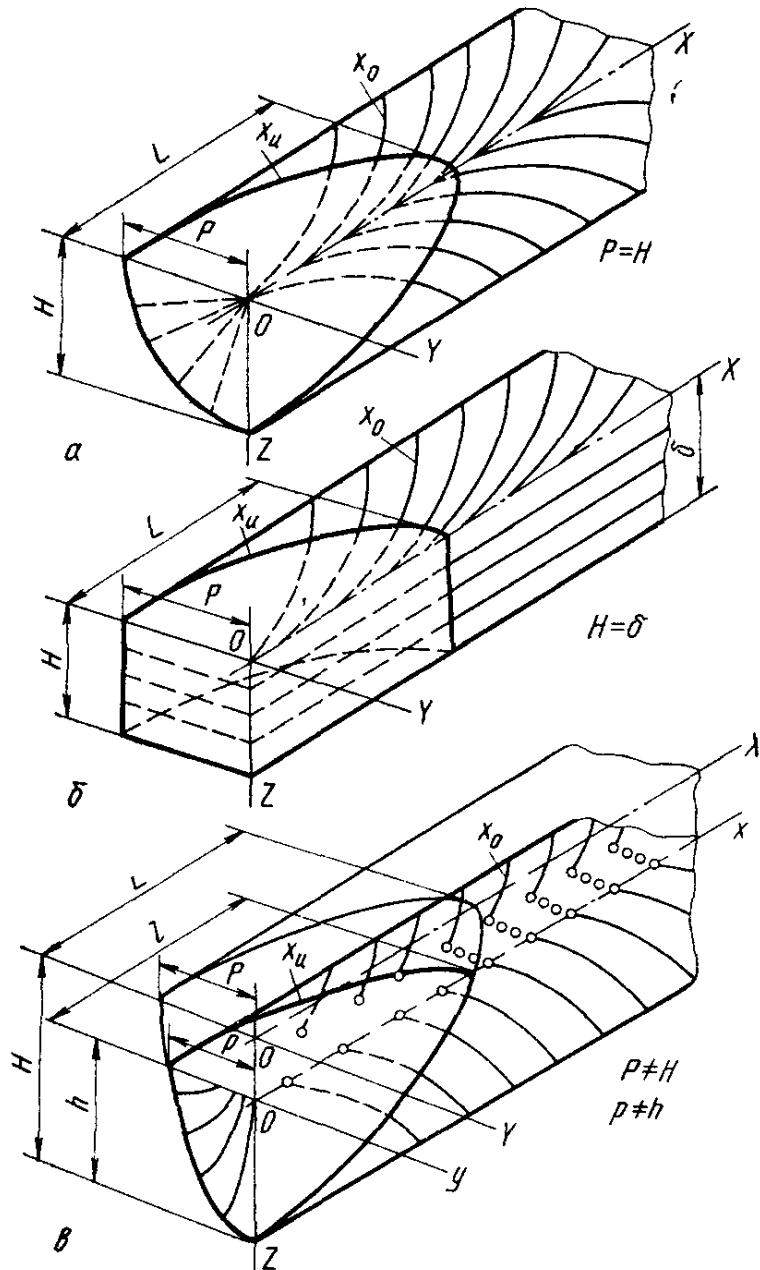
Форма осей кристаллитов при различном очертании сварочной ванны эллипсоидного типа:
